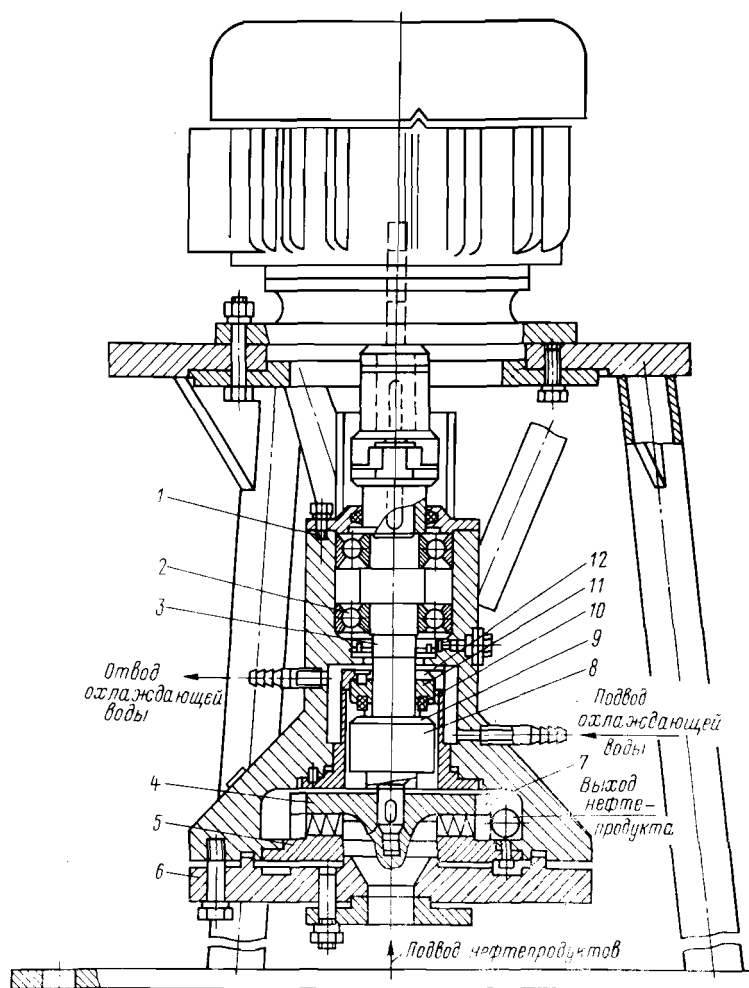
Схема гідродинамічного змішувача ГАРТ-ПЗМ: 1 - корпус; 2 - шарикопідшипники; 3 вал; 4 - ротор; 5 - упор; 6 - кришка; 7 - насосне колесо; 8 - торцеве ущільнення; 9 - кільце, що обертається; 10 - керамічне кільце; 11 - обойма; 12 - стакан
